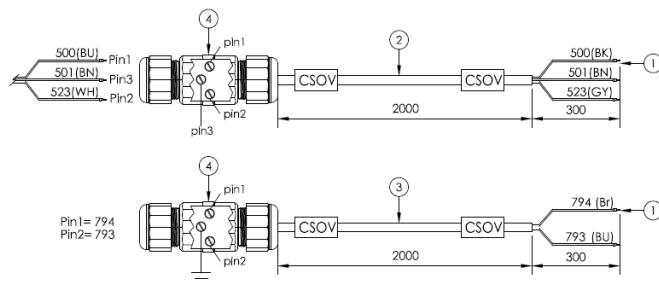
Schéma zapojení motoru (levý obrázek) a koncových spínačů (pravý obrázek)
